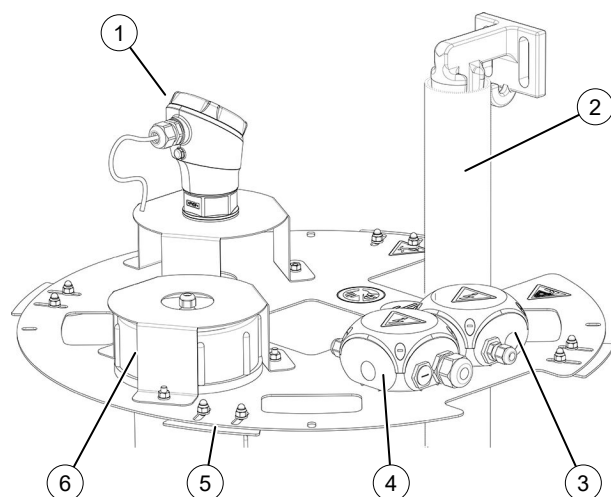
Plaque de fixation de capteurs cuve enterrée en PE
